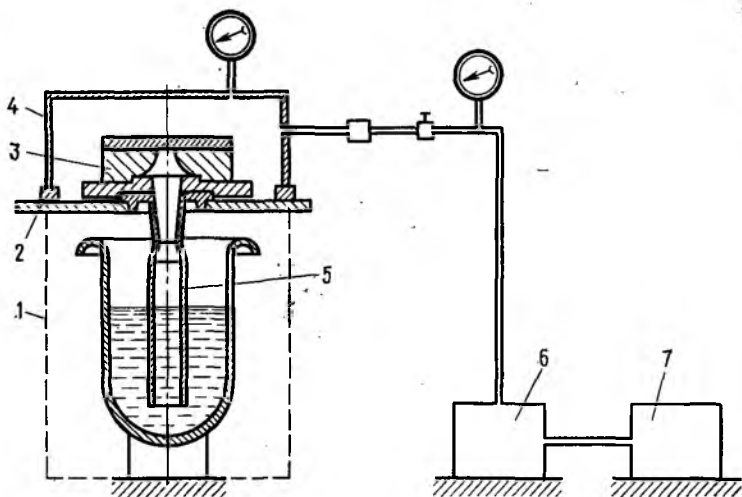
Схема установки для изготовления отливок вакуумным всасыванием
